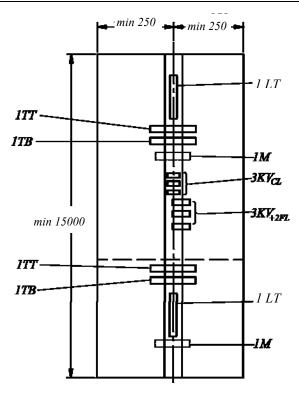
1 Butt weld test assembly for testing to approve electroslag and electrogas welding. Test specimens are designated according to 4.6.2.3 (All dimensions are in mm)
